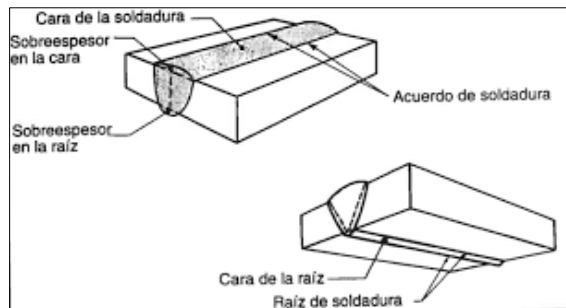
Refuerzo en raíz y cara de la soldadura
